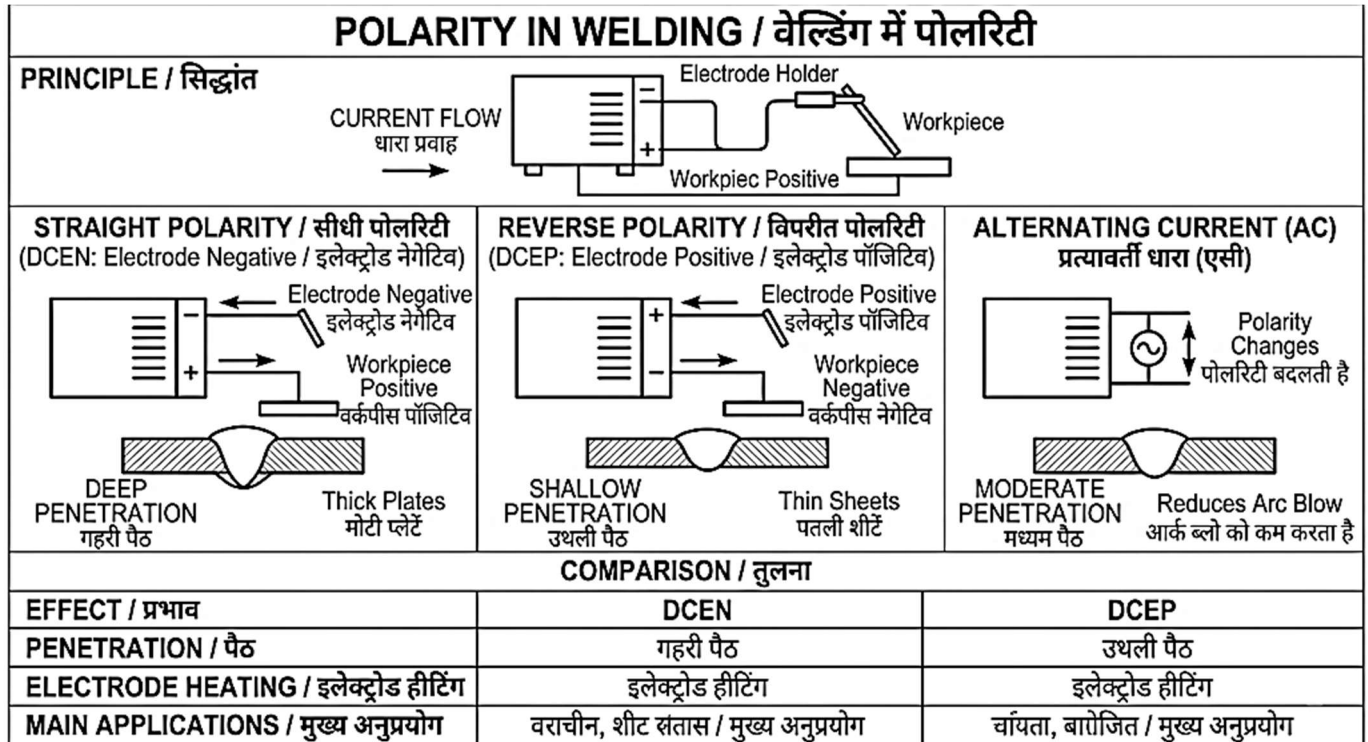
Welding Polarity and Current Types | वेल्डिंग पोलरिटी एवं धारा के प्रकार
